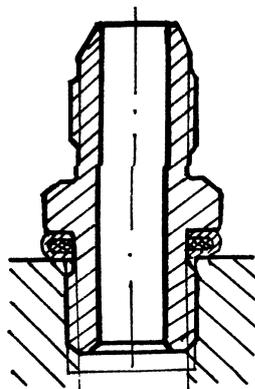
Уплотнение ввёртного штуцера армированной прокладкой
